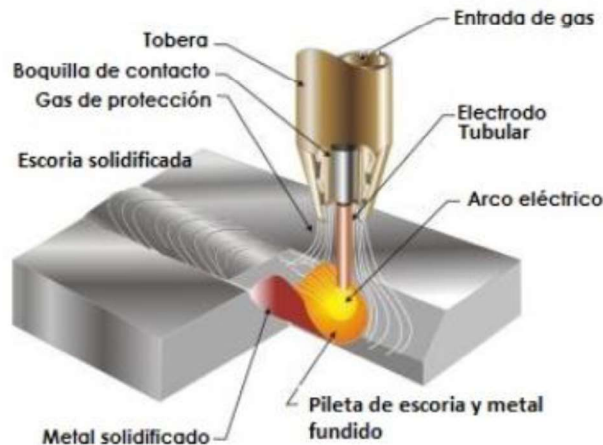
Proceso de soldadura de arco eléctrico (FCAW).
